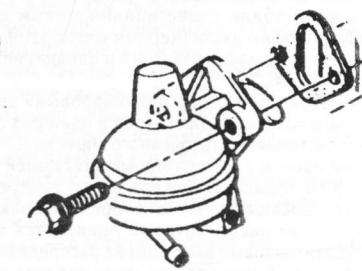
б Детали установки механического топливного насоса, используемого на моделях с четырехцилиндровым двигателем
